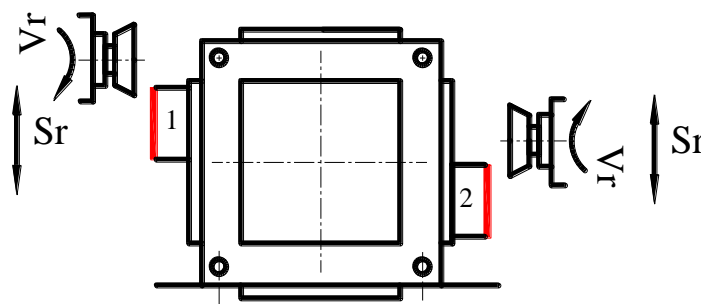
Эскиз наладки для варианта обработки двух деталей на спутнике призматической формы.
